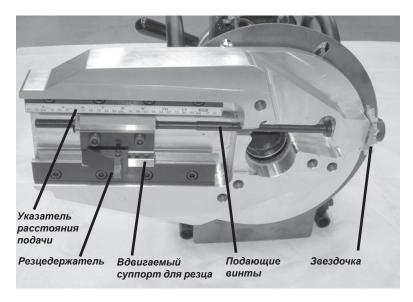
Однорезцовый суппорт обеспечивает радиальную подачу резца относительно поверхности трубы. Суппорт перемещается вдоль подающего винта при помощи звездочки.
